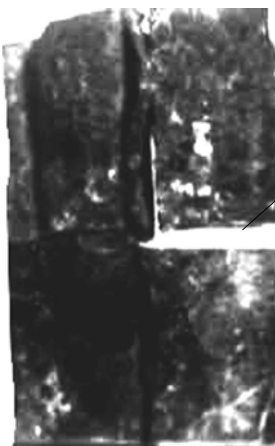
Характер руйнування фурми через низьку якість зварного шва (використовували мідь марки М0 [2] із залізом (використовували низьковуглецеву сталь марки НЖ) з різними
